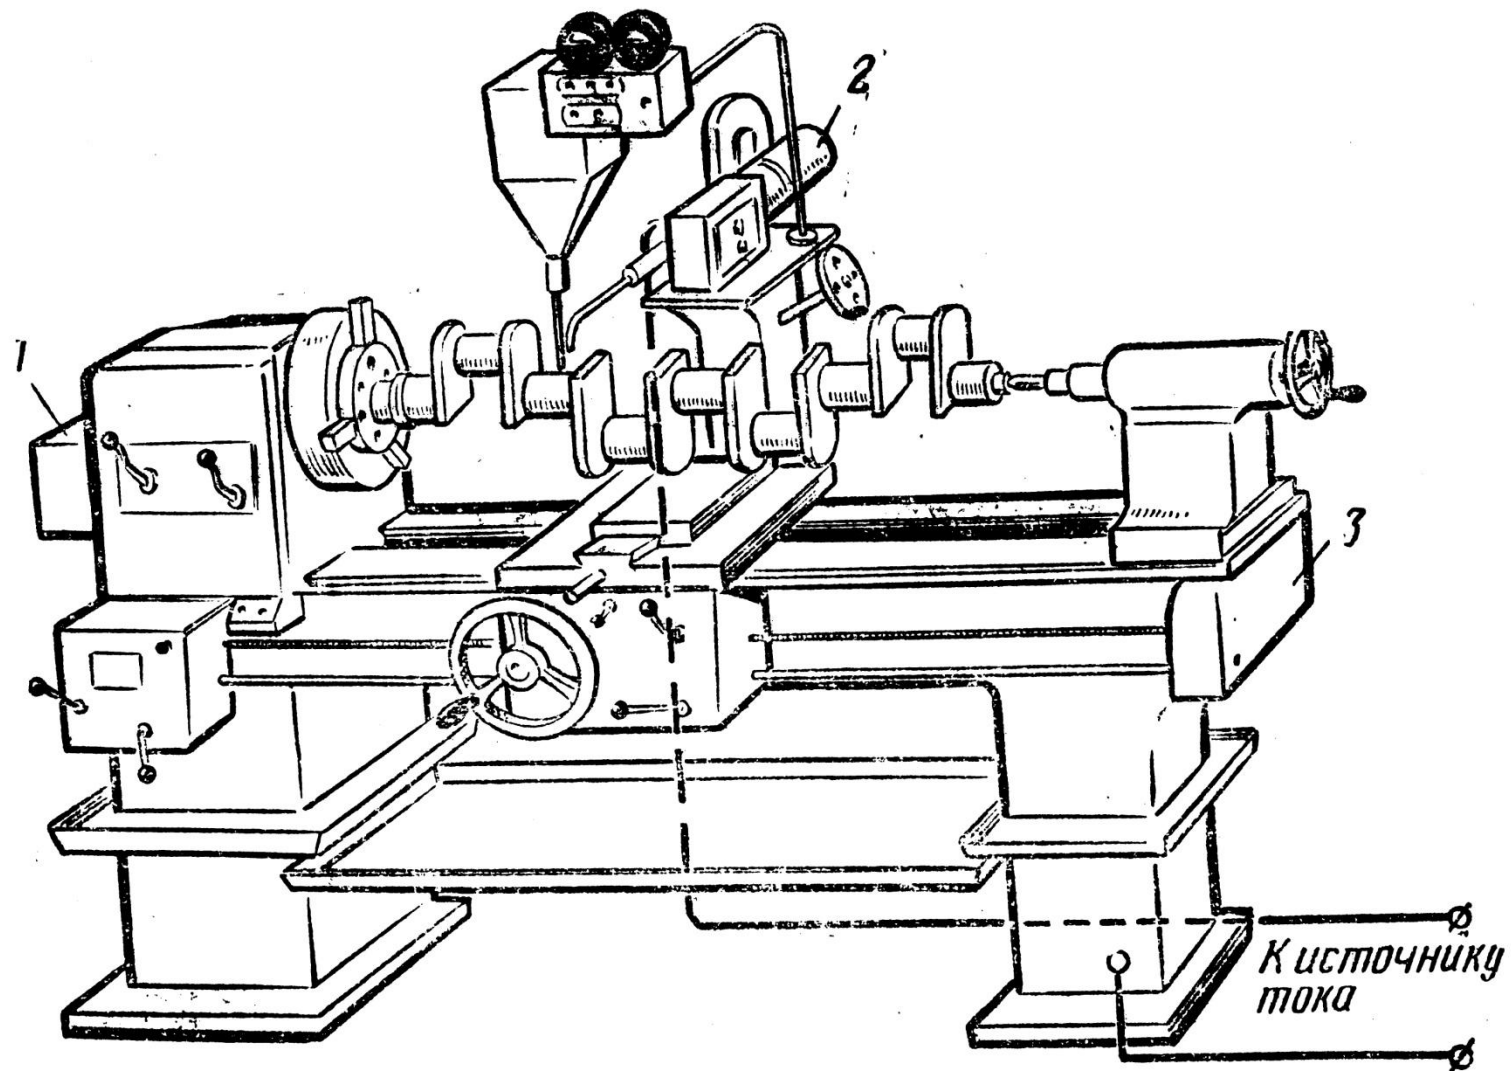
Установка для автоматической наплавки деталей под слоем флюса
